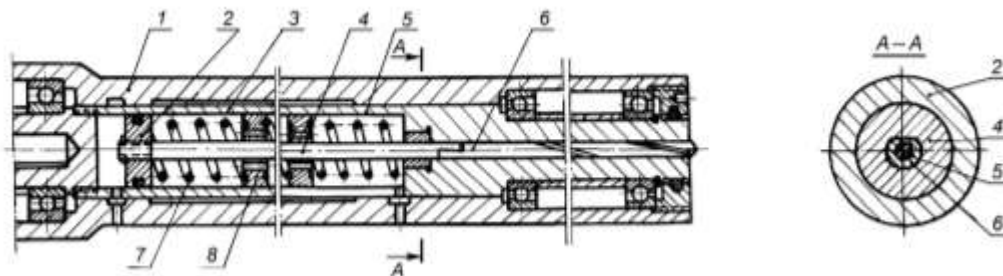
Конструкція механізму привода верстатів для глибокого свердління
